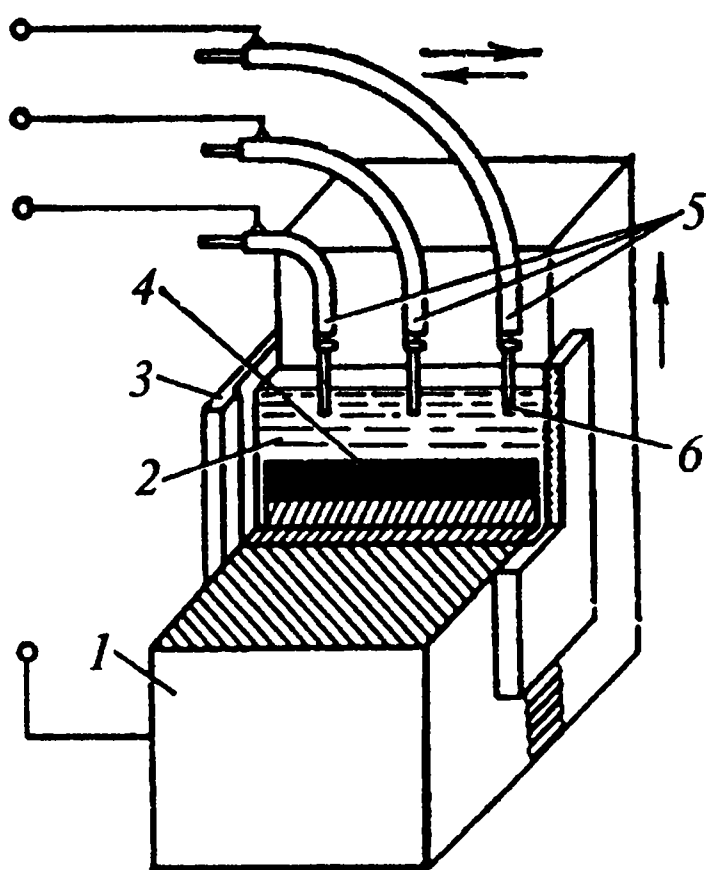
Схема процесса электрошлаковой сварки:
